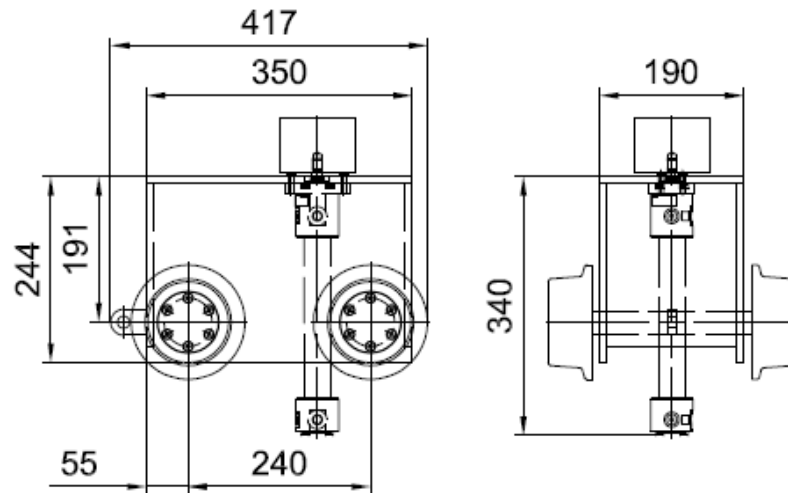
BG11; Position 2, Vorderansicht und Seitenansicht
